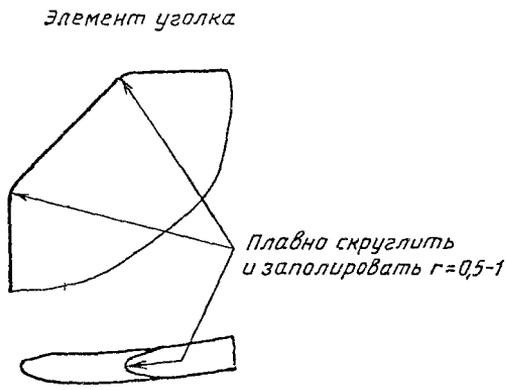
Обрезка уголков лопаток I ступени компрессора
